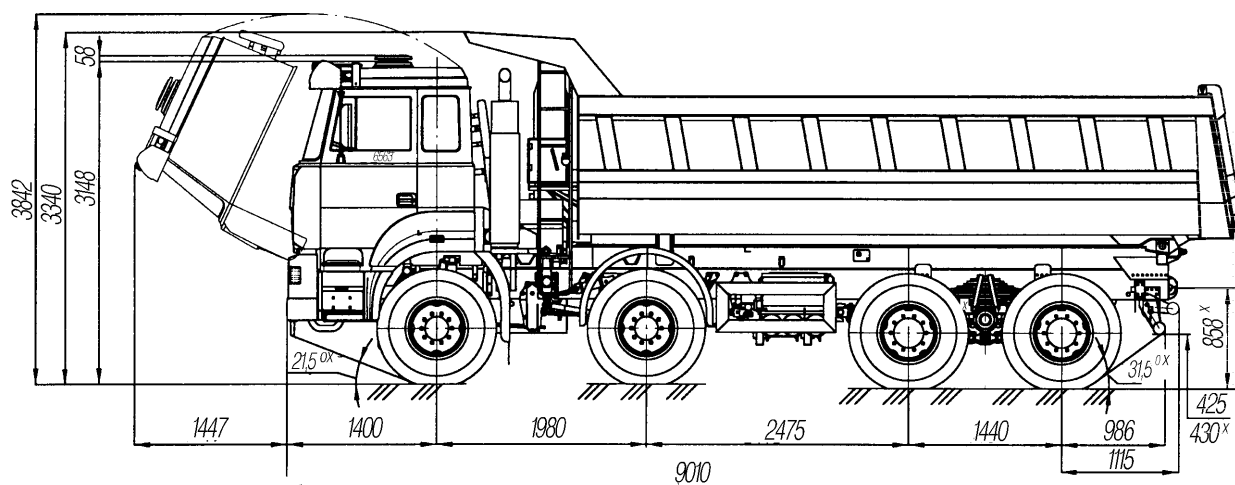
Габаритные размеры автомобиля Урал-6563
